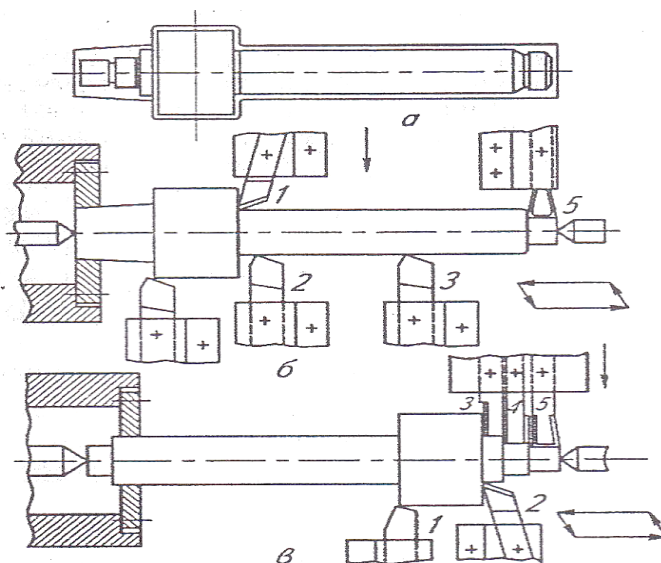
Схема обработки вала-шестерни на многорезцовом станке:
